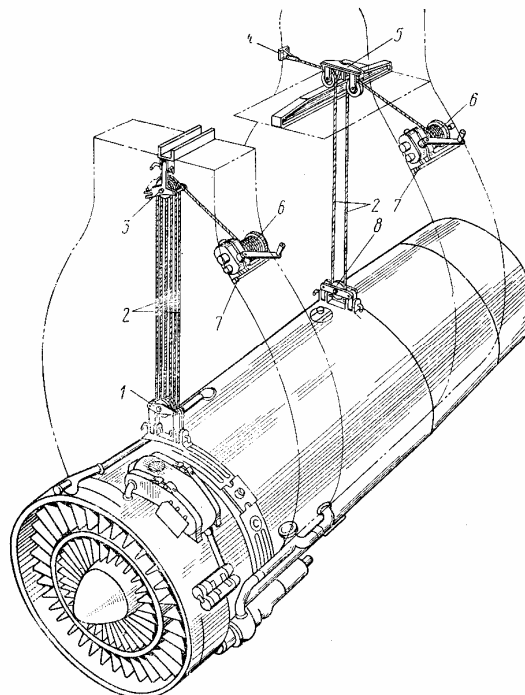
Приспособление 154.00.9960.030 для монтажа среднего двигателя:
